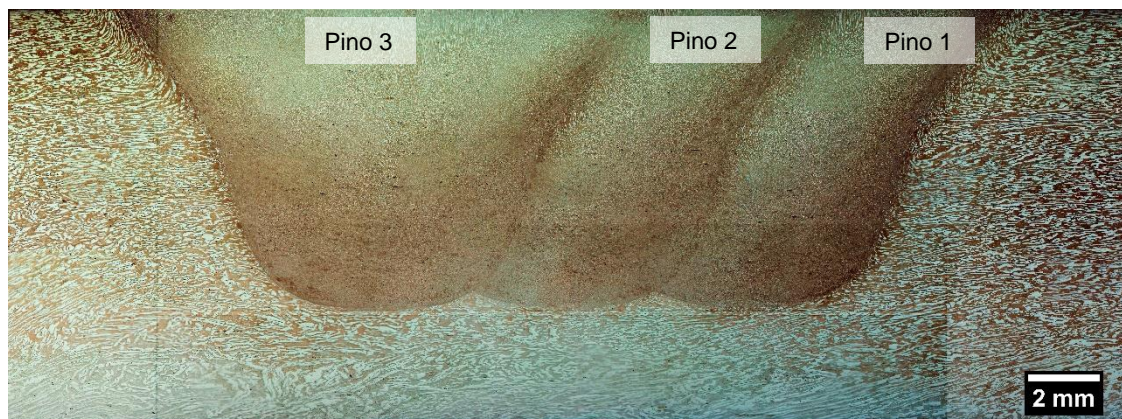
Macrografia extraída após soldagem SCF com passo 1/3D. (Vista em corte).
